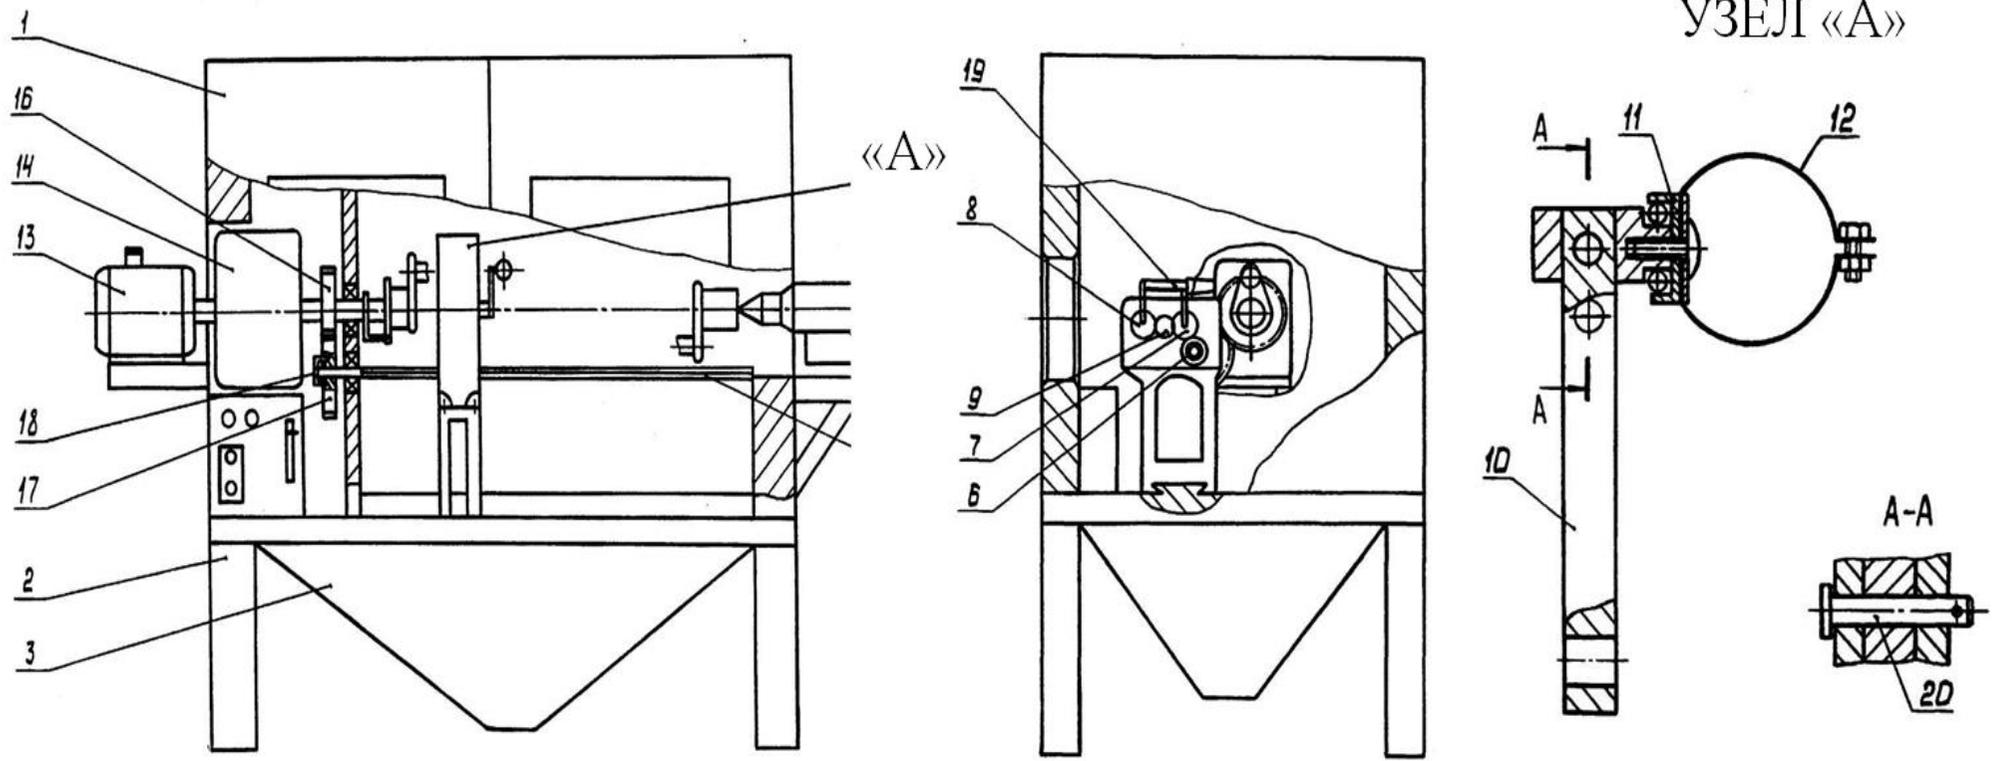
Схема устройства для восстановления шеек коленчатых валов
